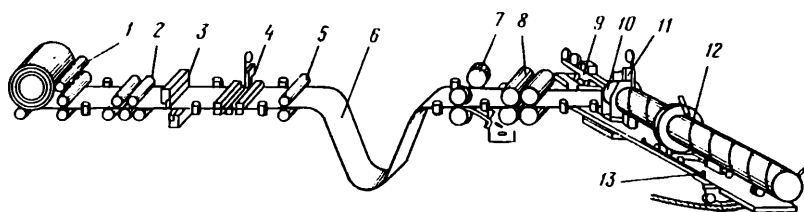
Схема расположения оборудования трубозлектросварочного стана 1020 для изготовления спиральношовных труб
